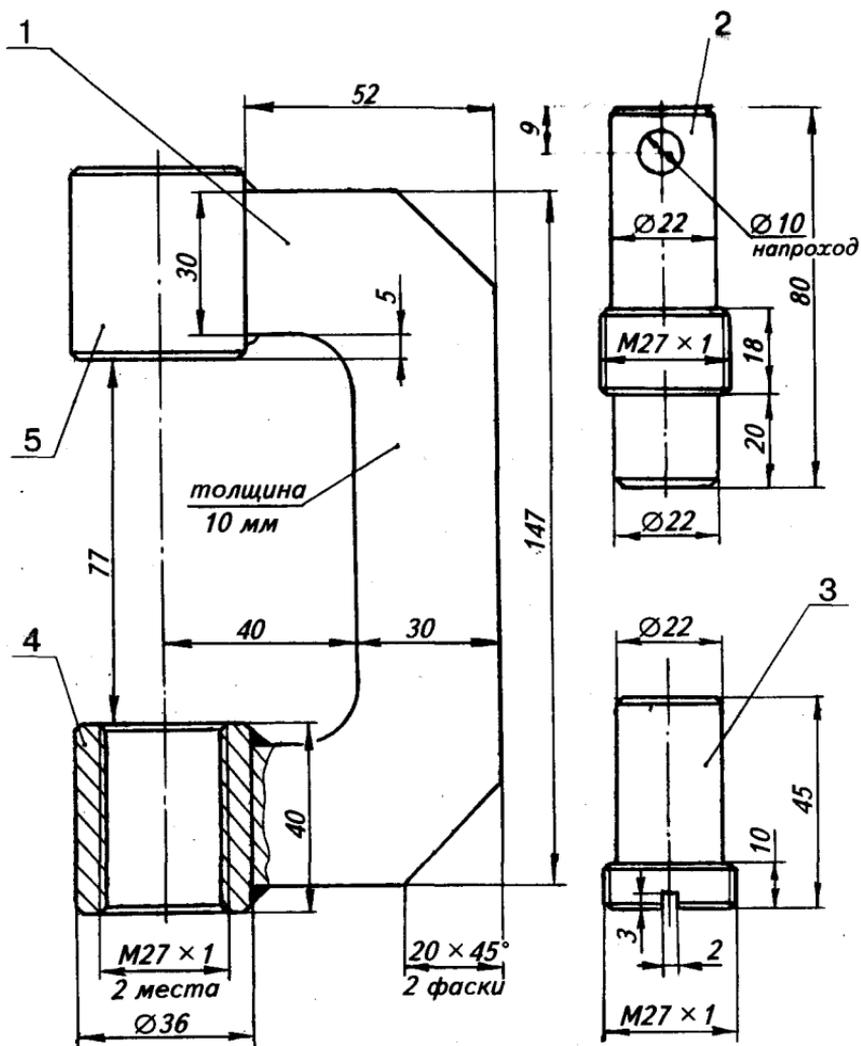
Приспособление для выпрессовывания и запрессовывания подшипников карданного вала:
